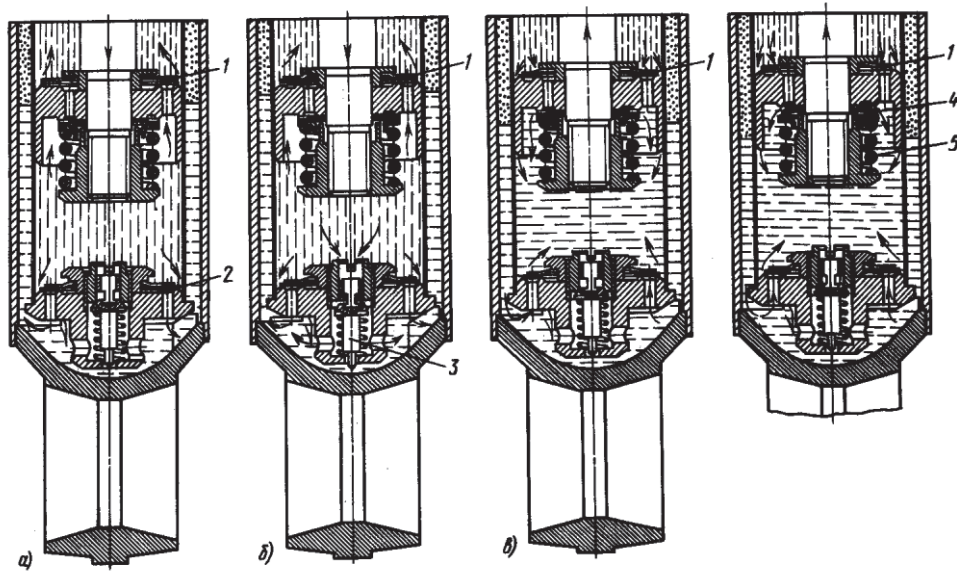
Робочий процес двотрубного телескопічного амортизатора:
